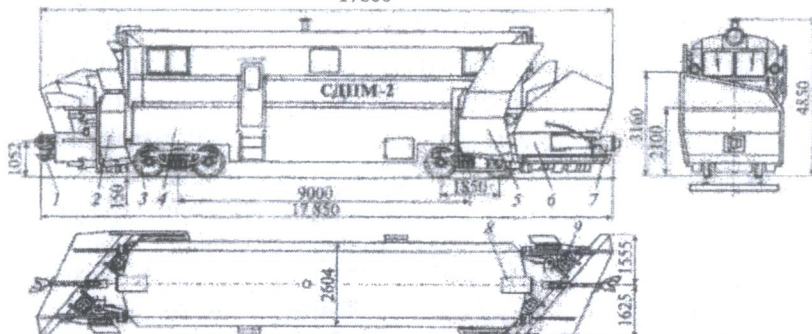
СДПМ-2: 1 – подрезной нож; 2 и 5 – угловое и боковое крылья; 3 – ходовая тележка; 4 – корпус; 6 – лобовой щит; 7 – выдвигающая авто-сцепка; 8 –прожектор
